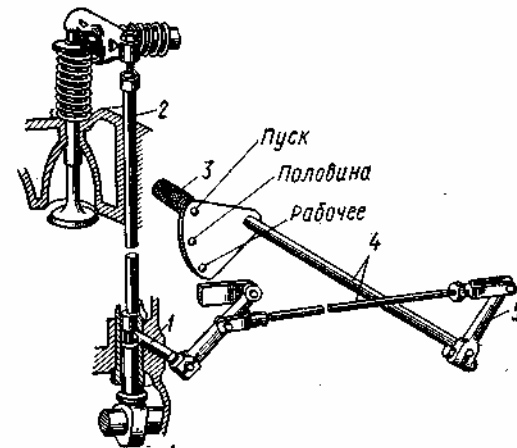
Декомпрессионный механизм четырехцилиндрового дизеля
